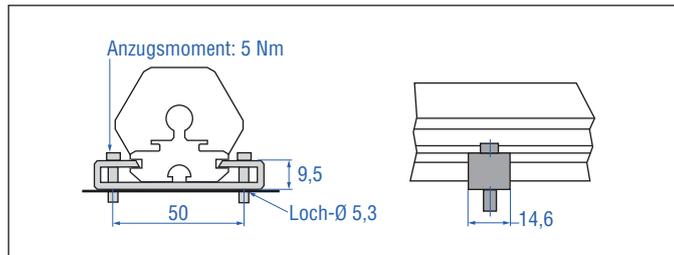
Montageklammern (Artikelnr. 400 802) mit Zylinderschraube M5×20
